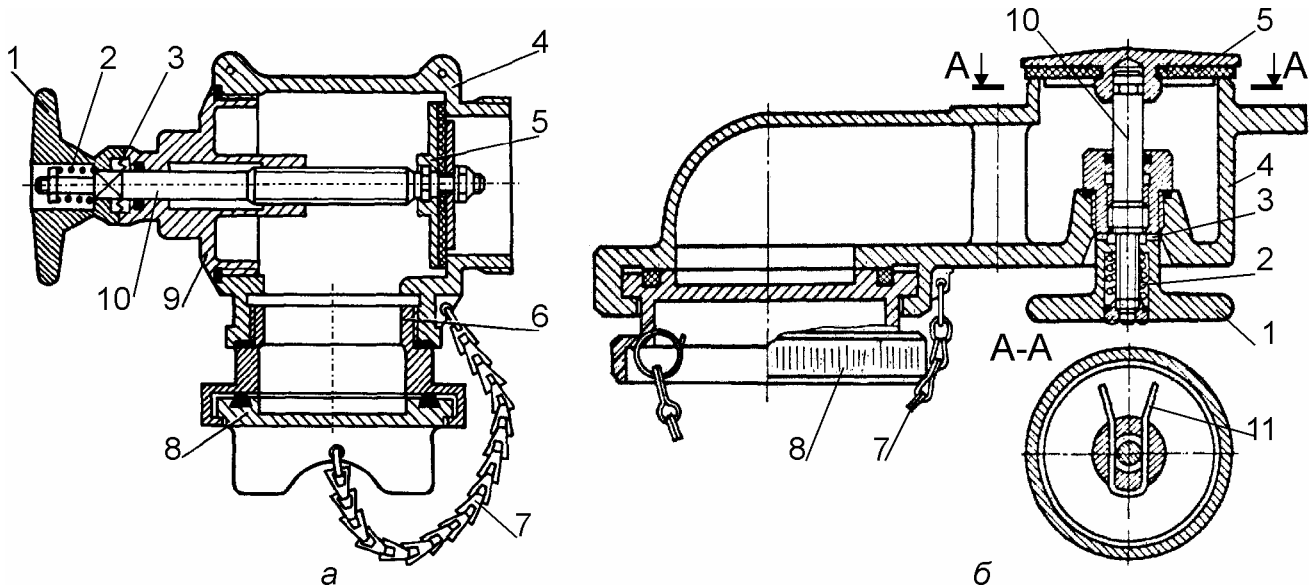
Крани зливання: а — 604700 (Ан-124); б — 90-6107-20 (Ми-26);
